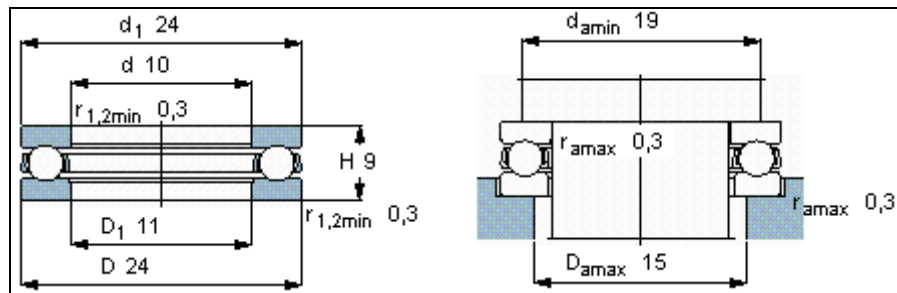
Rodamiento axial de bolas seleccionado⁴²
